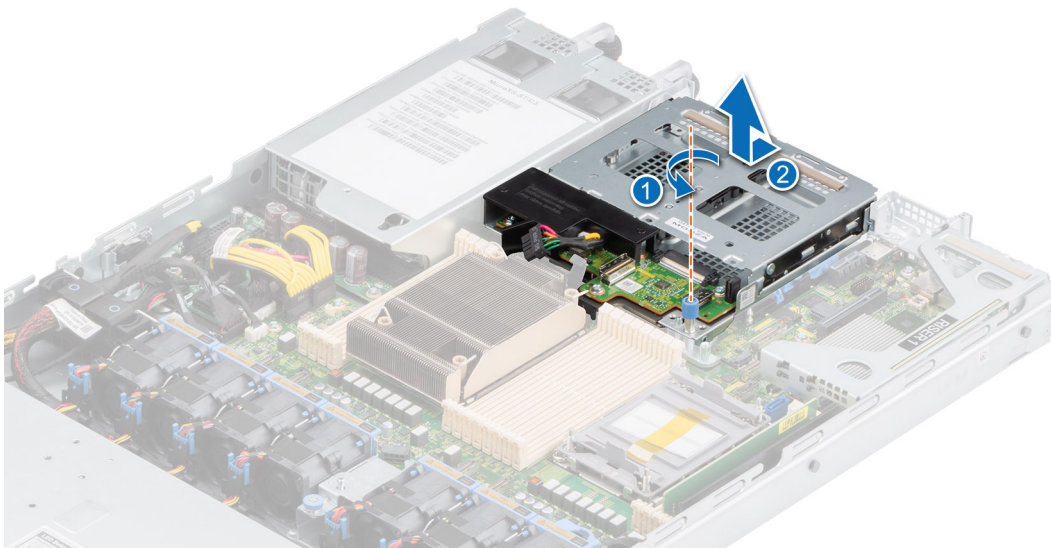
Entfernen des hinteren 2,5-Zoll-Laufwerksgehäuses
